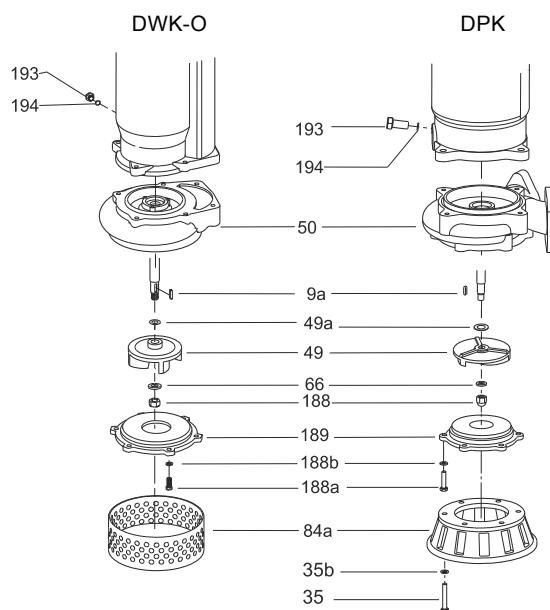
Демонтаж рабочего колеса и корпуса насоса.
